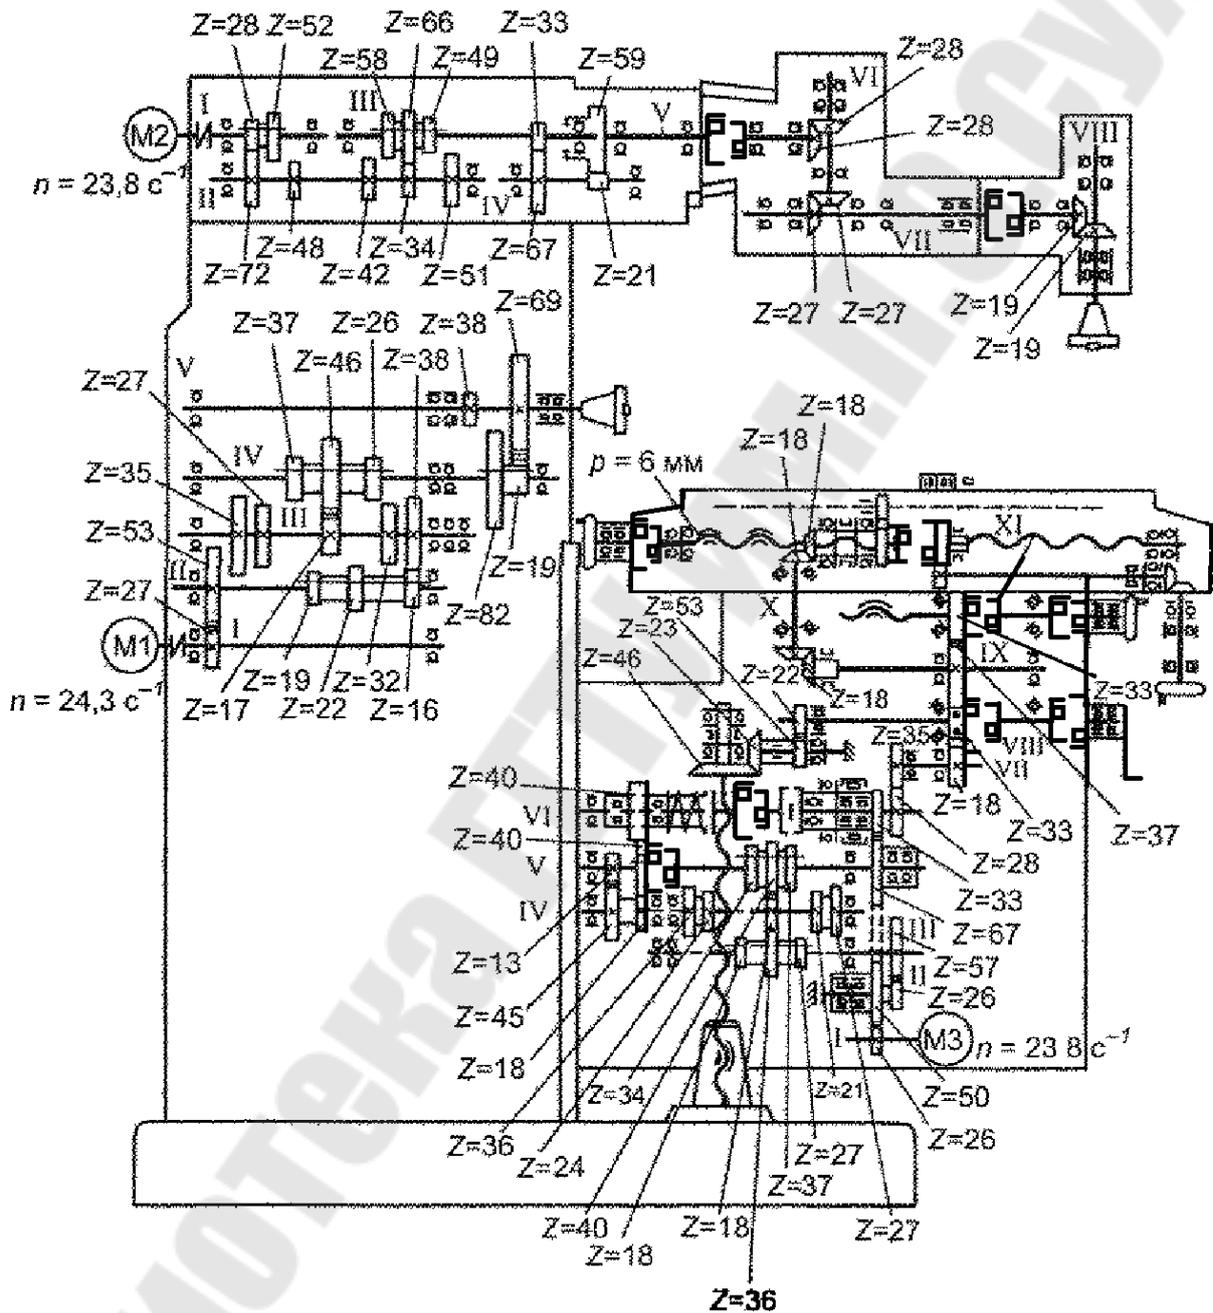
Кинематическая схема широкоуниверсального консольного фрезерного станка
